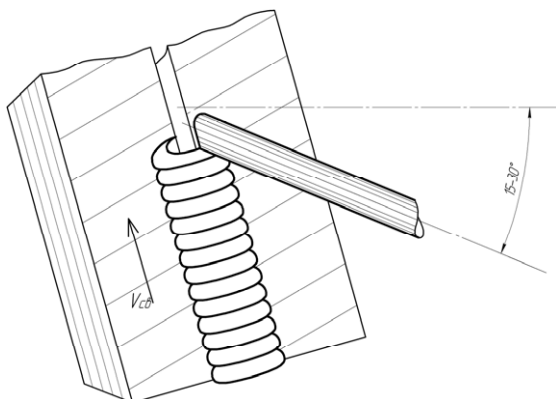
Схема заварки трещины в полувертикальном положении
